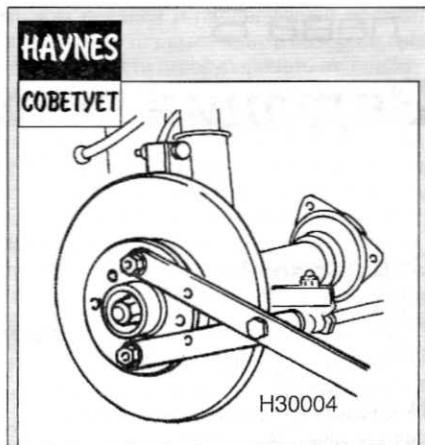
Установив удерживающий инструмент, с помощью торцевой головки и удлинителя отверните гайку крепления полуоси
